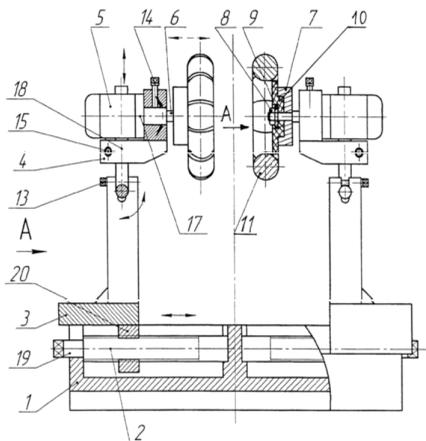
Конструкция предлагаемого устройства для магнитно-абразивной обработки (вид сбоку)
